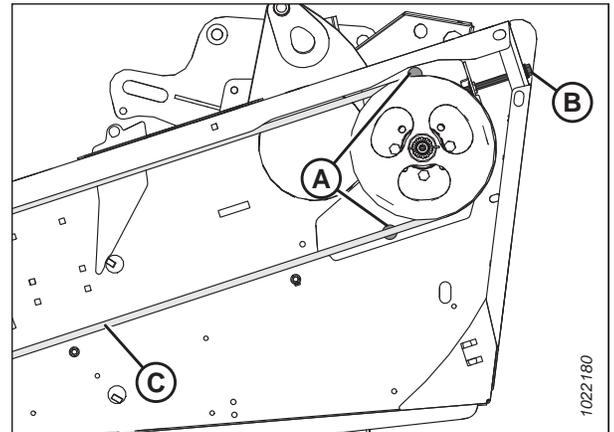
Moteur d'entraînement des couteaux et dispositif de réglage
